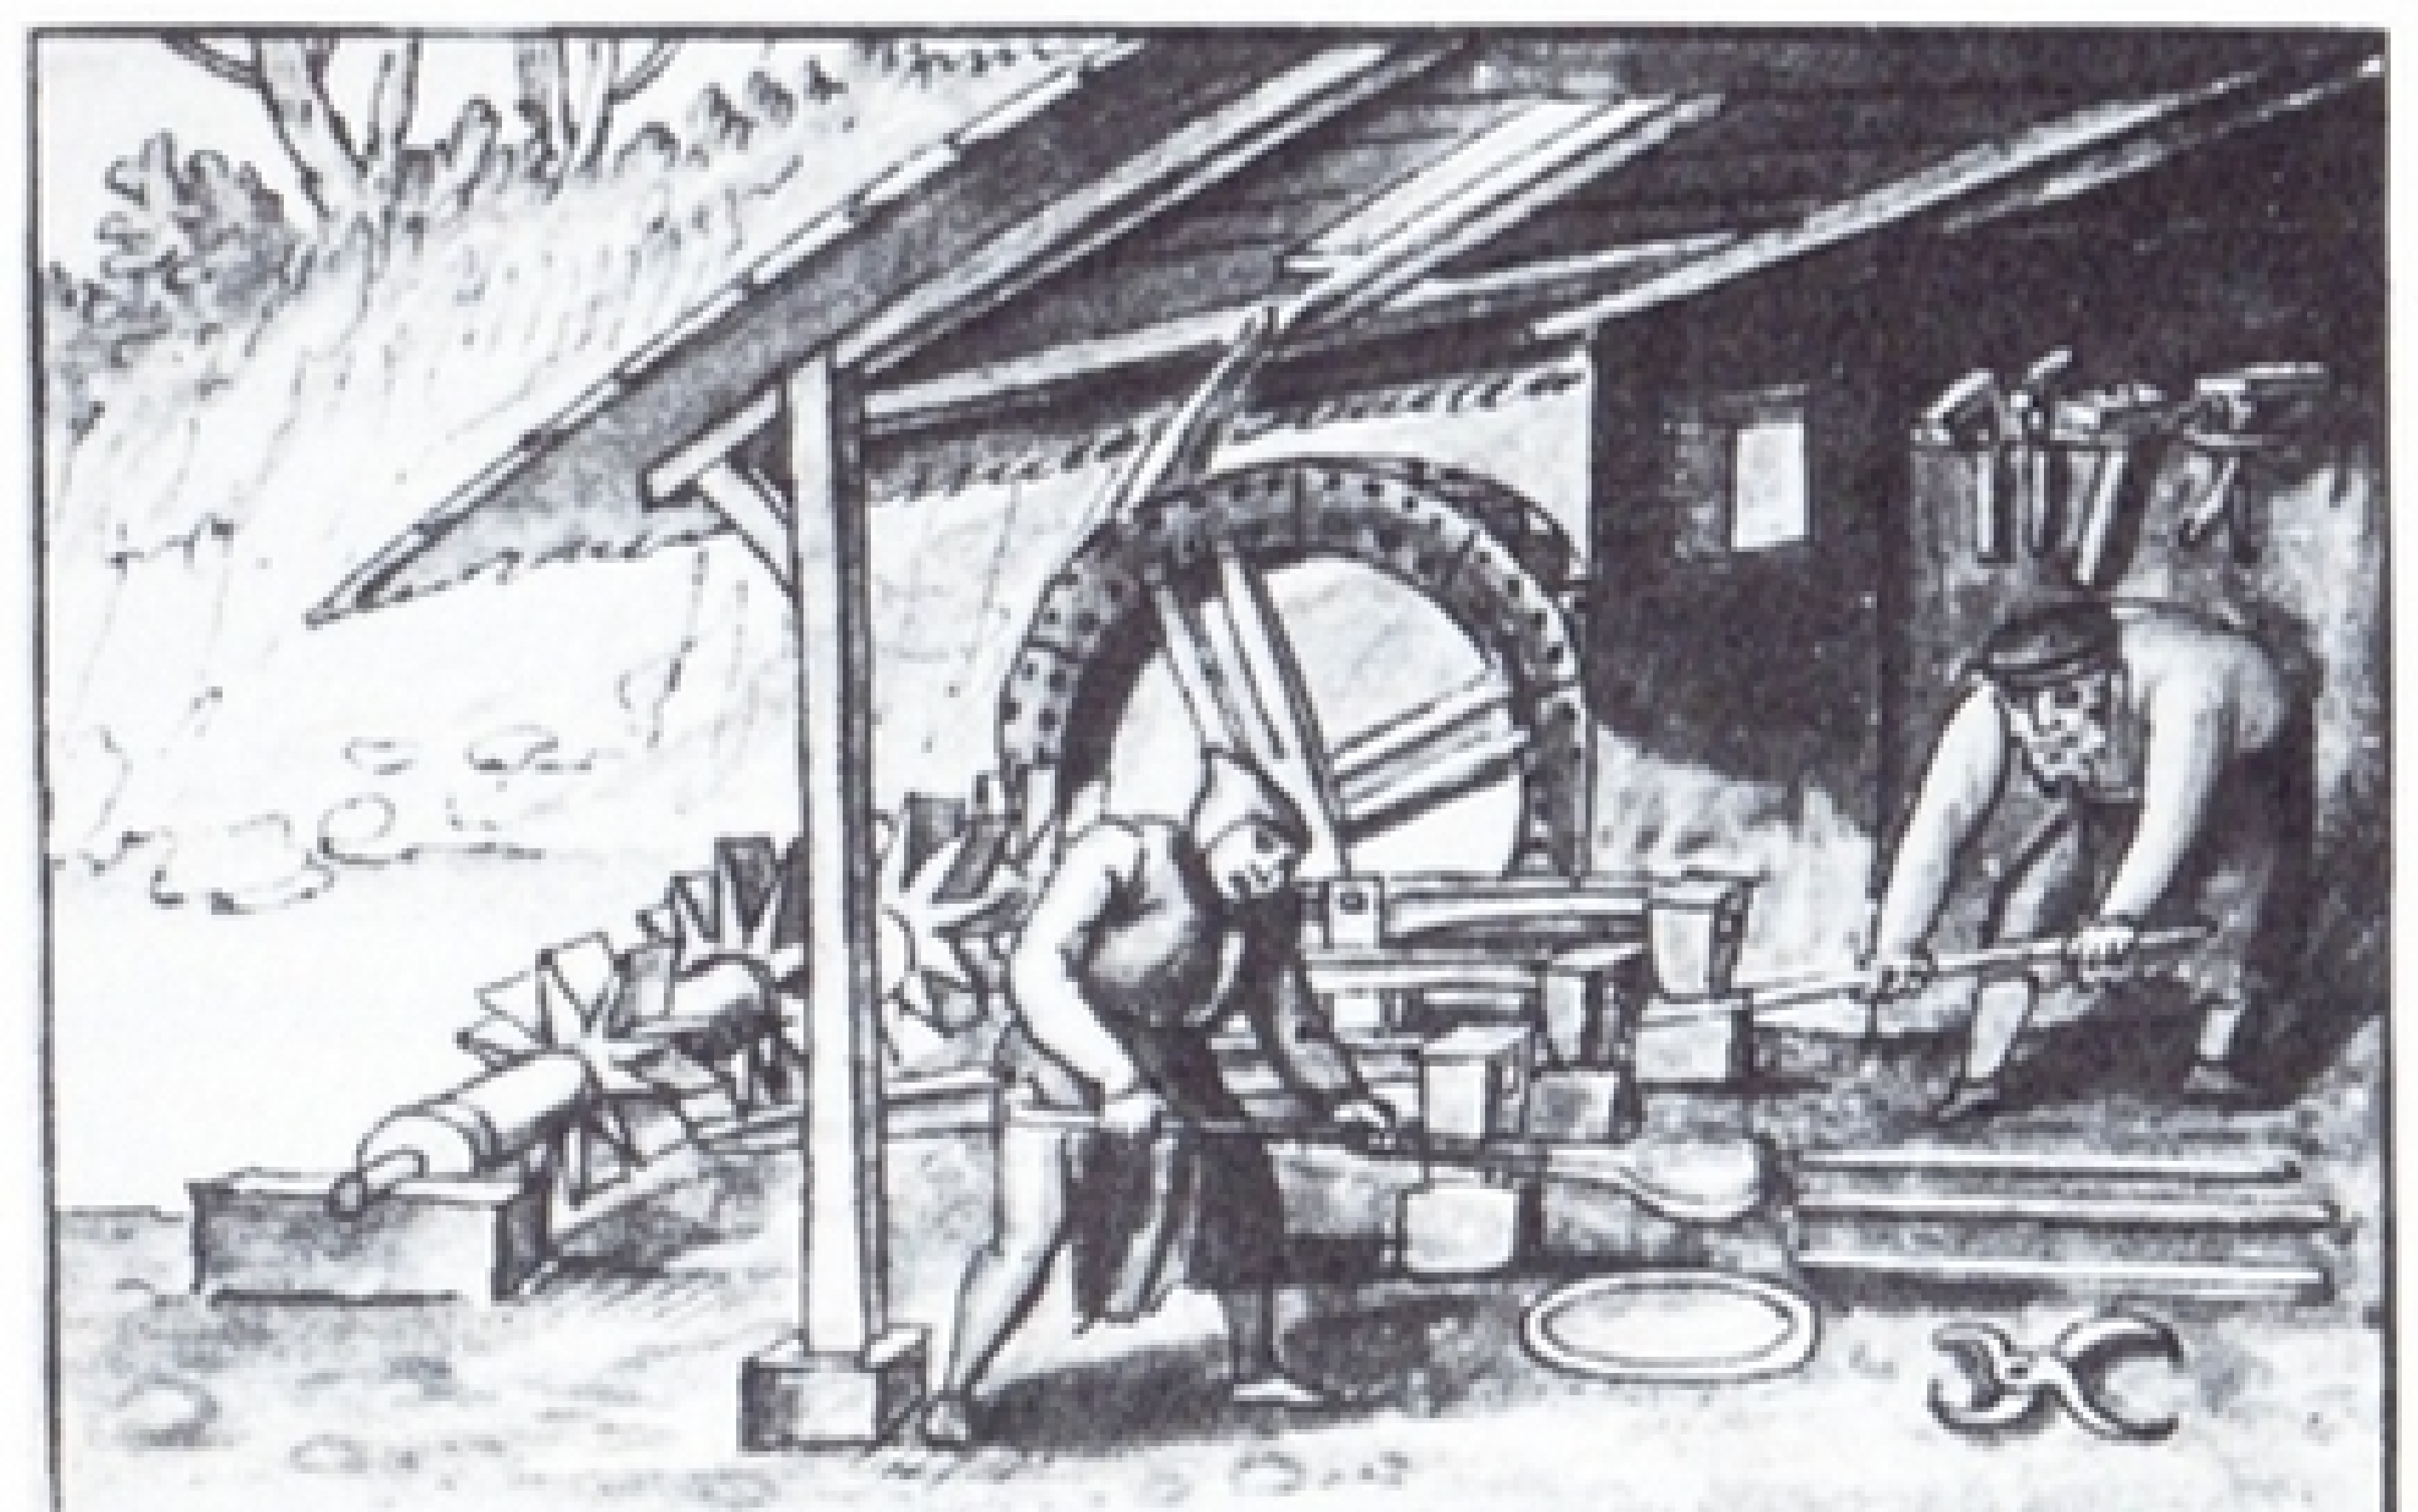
Hammerwerk mit Wasserradantrieb (Foto: Deutsches Museum, München)
